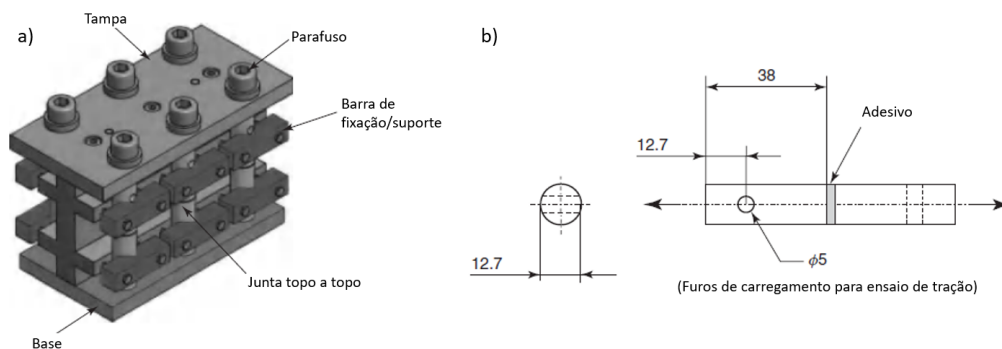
(a) Molde para o fabrico de juntas topo a topo e (b) Geometria do provete (dimensões em mm), adaptado de [15]
